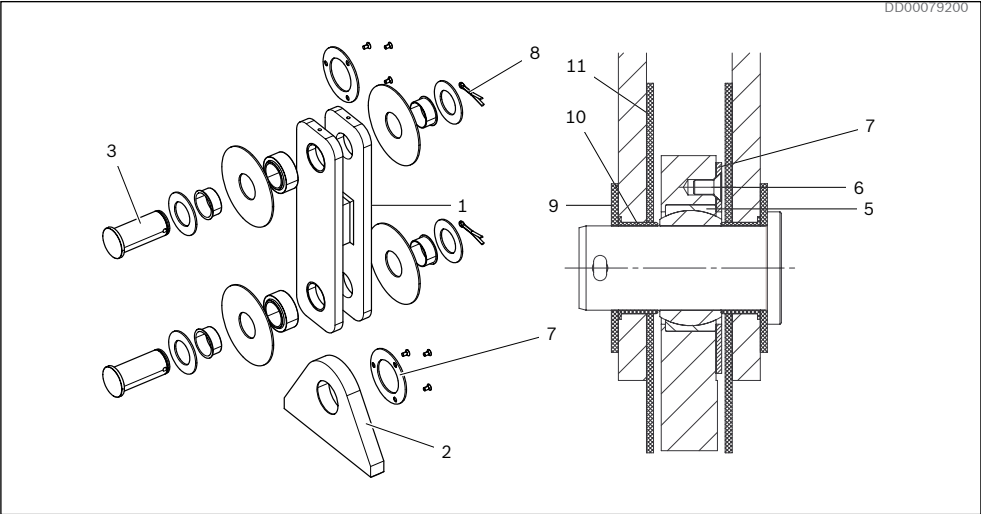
Conexión articulada TC A con aislamiento eléctrico
